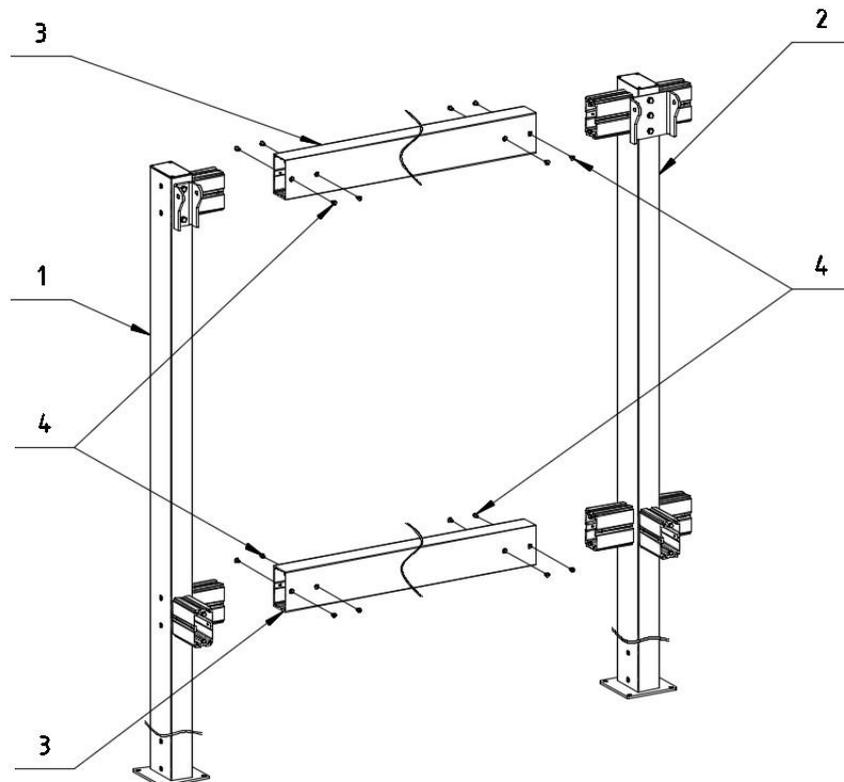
Méthode d'installation de la poutre arrière du premier module. 1 - Poteau haut (gauche/droite), 2 - Poteau haut (intermédiaire), 3 - Poutre arrière, 4 Vis M8x16.
